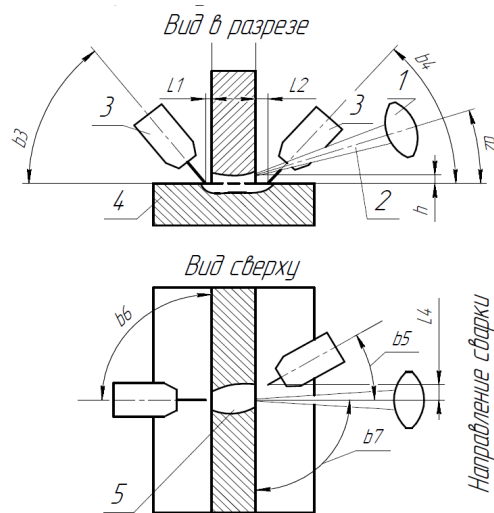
Схема ГЛДС, метод «Гибрид двусторонний» стыкового сварного соединения в горизонтальном положении (РС):
